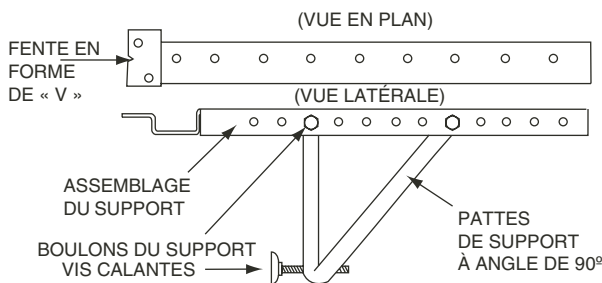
ASSEMBLAGE DU SUPPORT
